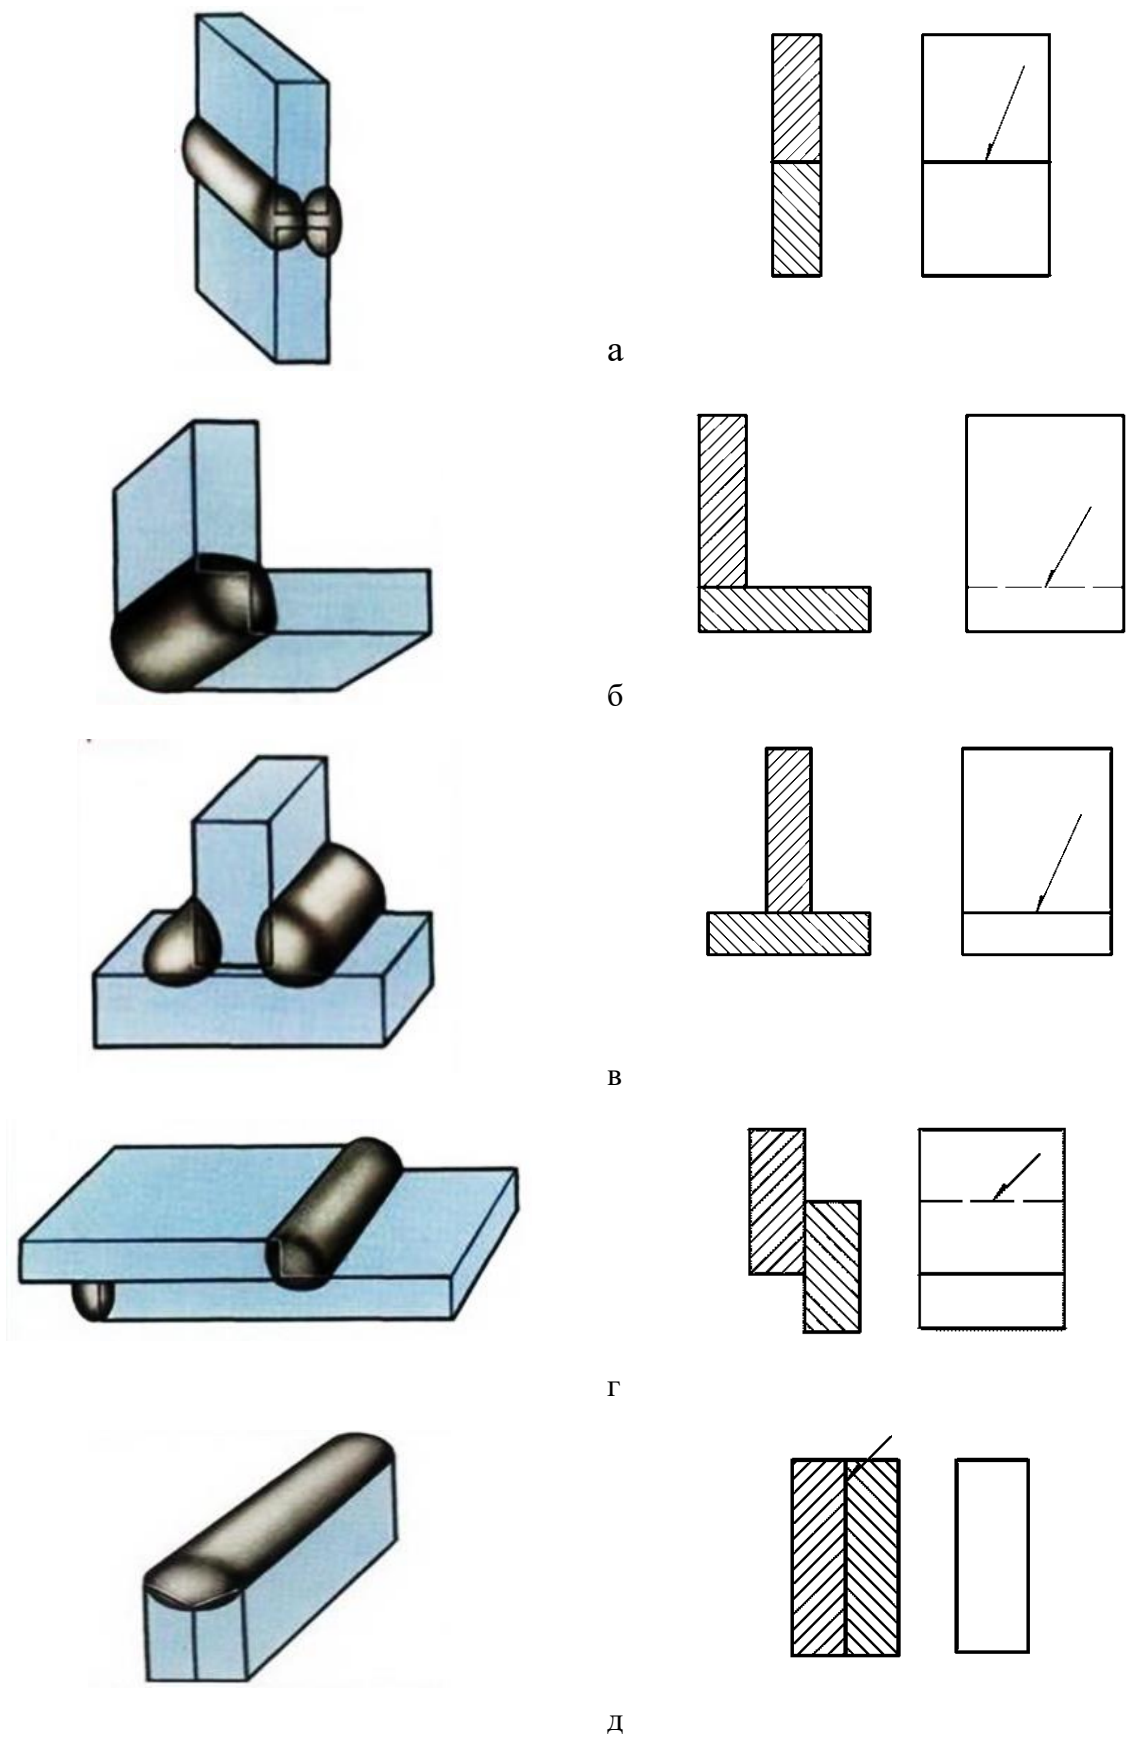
Виды сварных соединений: а-стыковое; б- угловое; в- тавровое; д- нахлесточное; д- торцовое.
